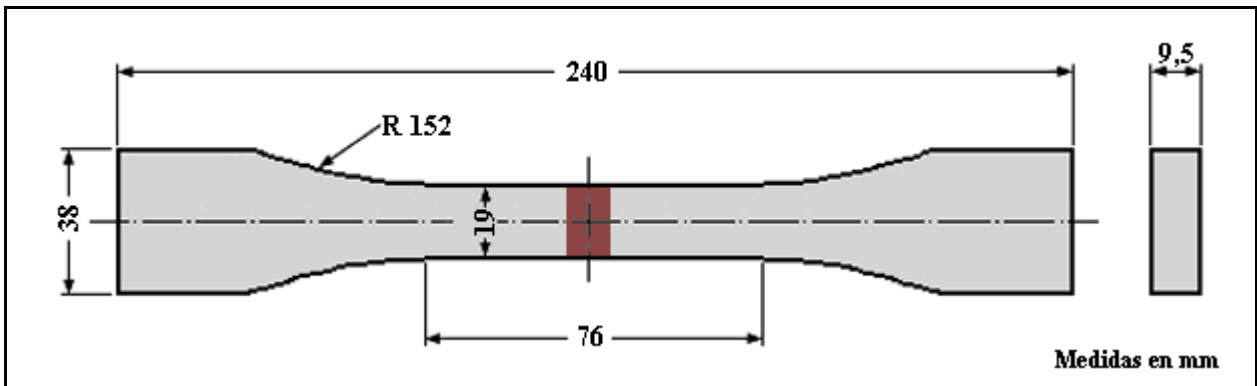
Medidas de la probeta de fatiga con soldadura transversal de acuerdo a la norma ASTM E466 – 76.
